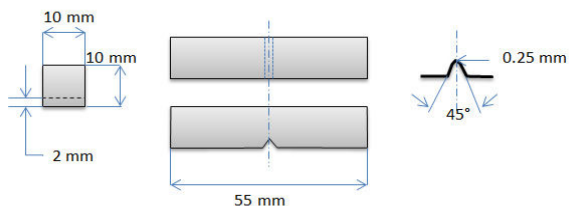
Geometria e dimensões de provetes de impacto Charpy, tipo A.
